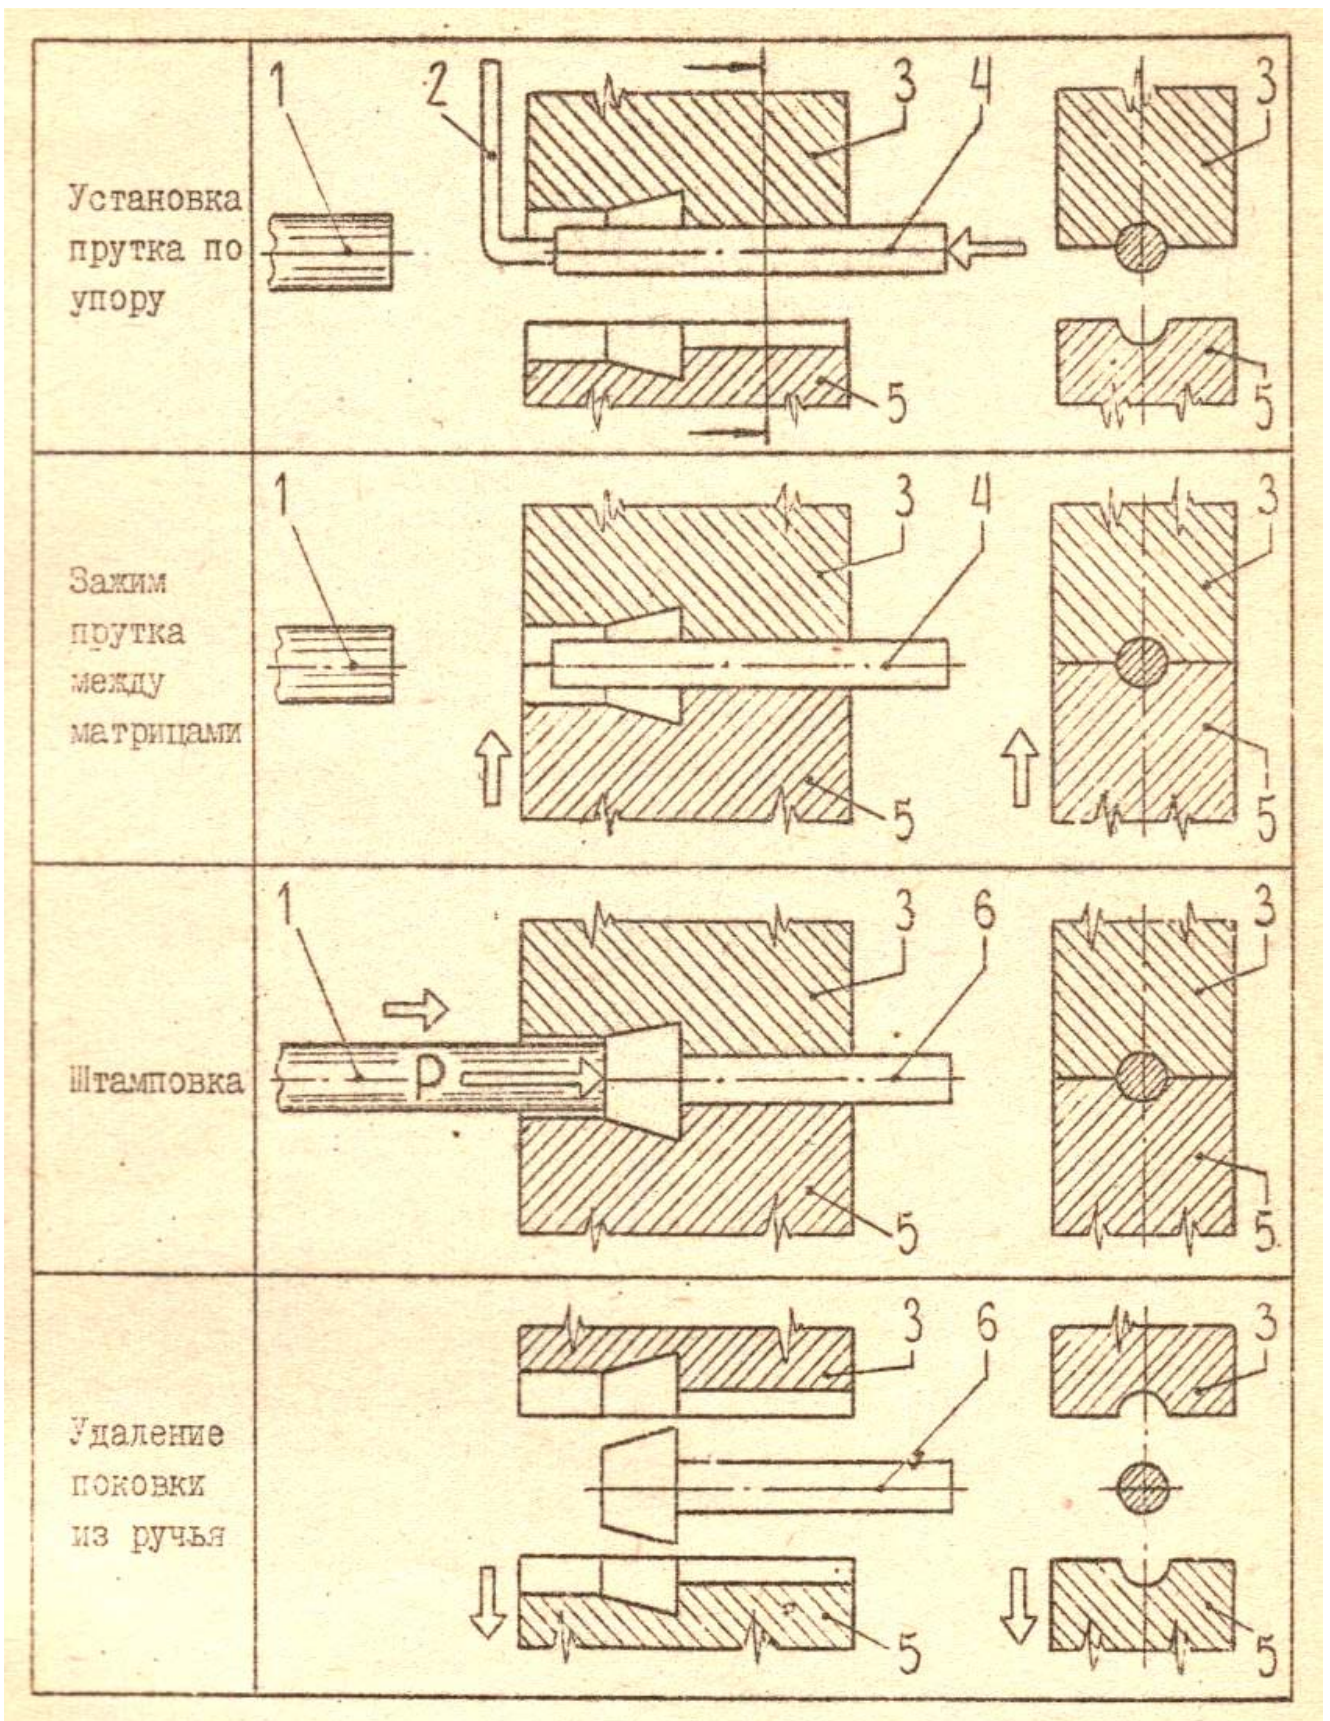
Последовательность операций при штамповке в одном ручье: 1 — пуансон; 2 — упор отводной; 3 — неподвижная матрица; 4 — заготовка; 5 — подвижная матрица; 6 — поковка
